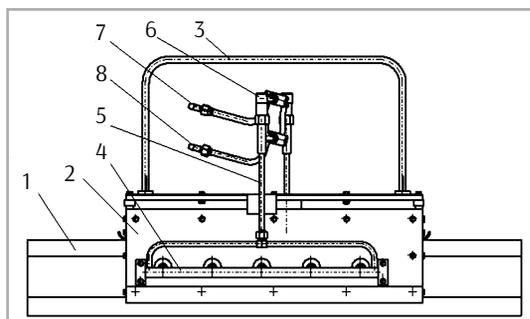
Чертеж переносной установки для нагрева рельсового пути УНР-ЖД
